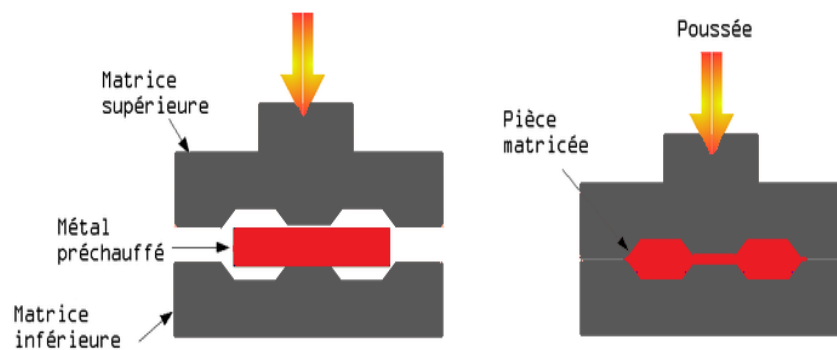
Schéma d'élaboration par forgeage (pièces forgées).
